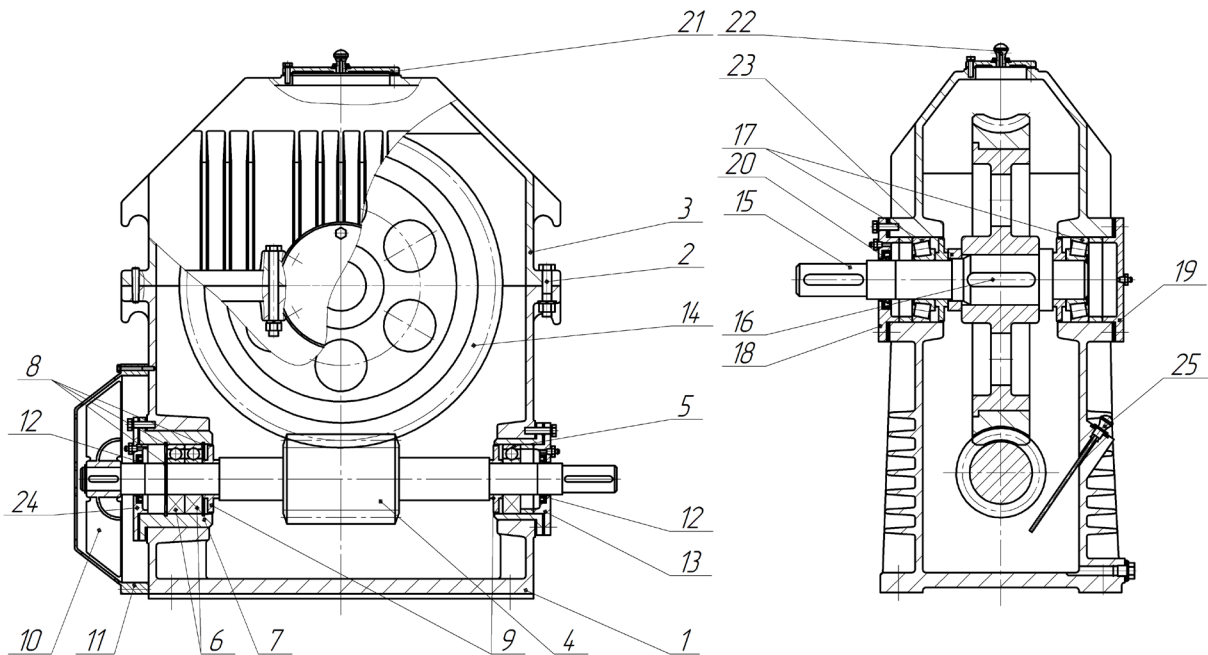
Конструкція черв'ячного редуктора з нижнім розташуванням черв'яка
